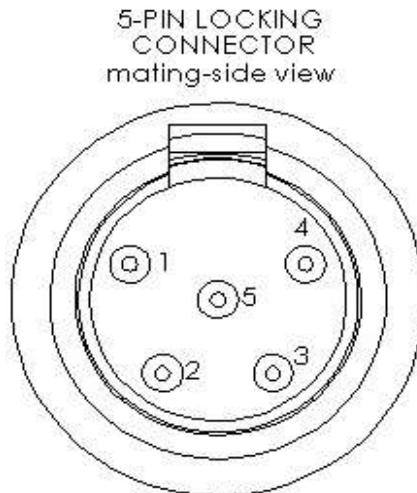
5poliger Stecker des CBL 203 oder CBL208 in direkter Draufsicht
